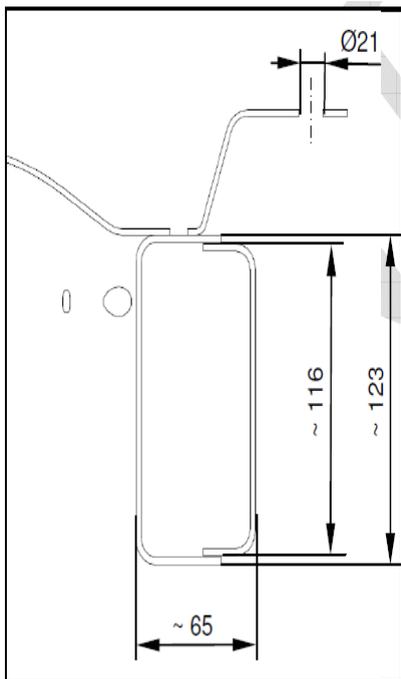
coupe S-S (Amarok SC/DC)
